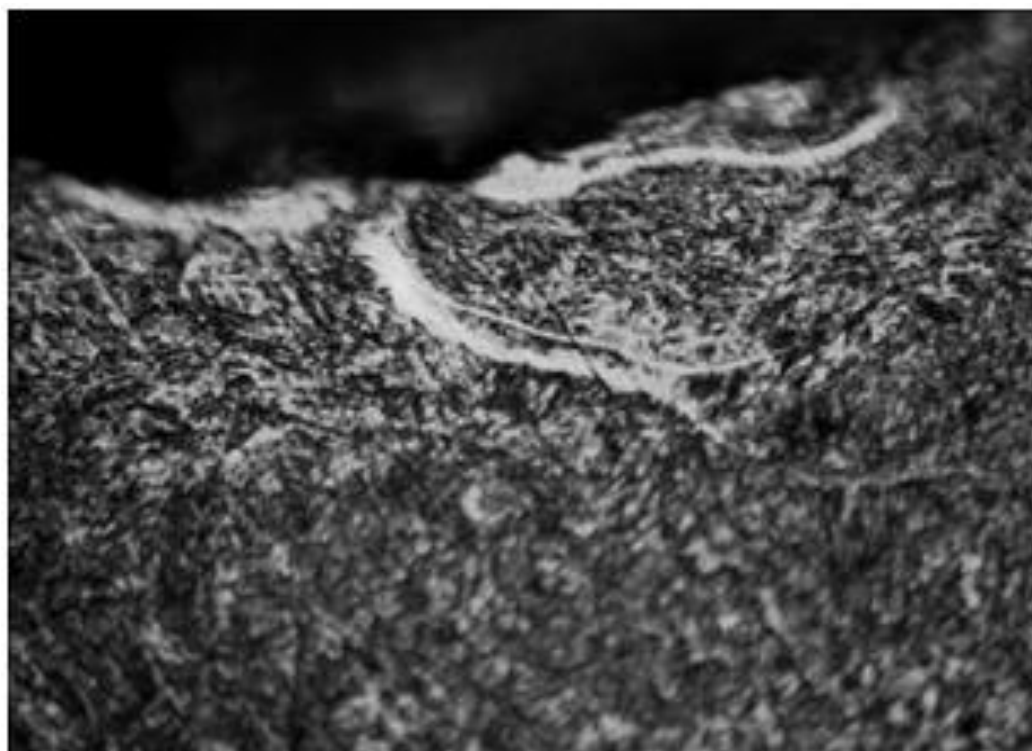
Волосовидные трещины на торцевой поверхности детали "втулка".
